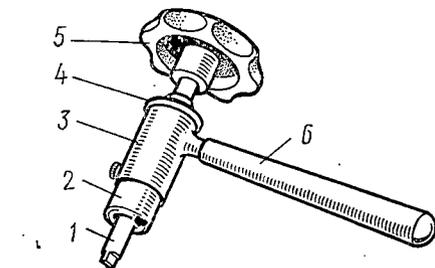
Приспособление ПИМ-4816 для регулировки зазоров в клапанах:
